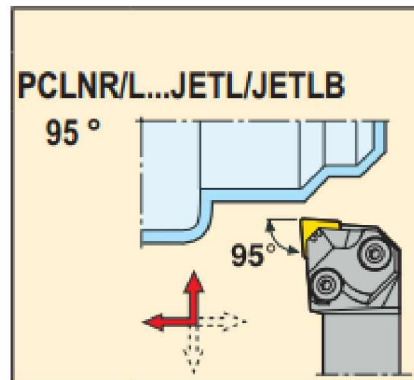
Різець для зовнішньої обробки з ромбічною пластиною SCMT
